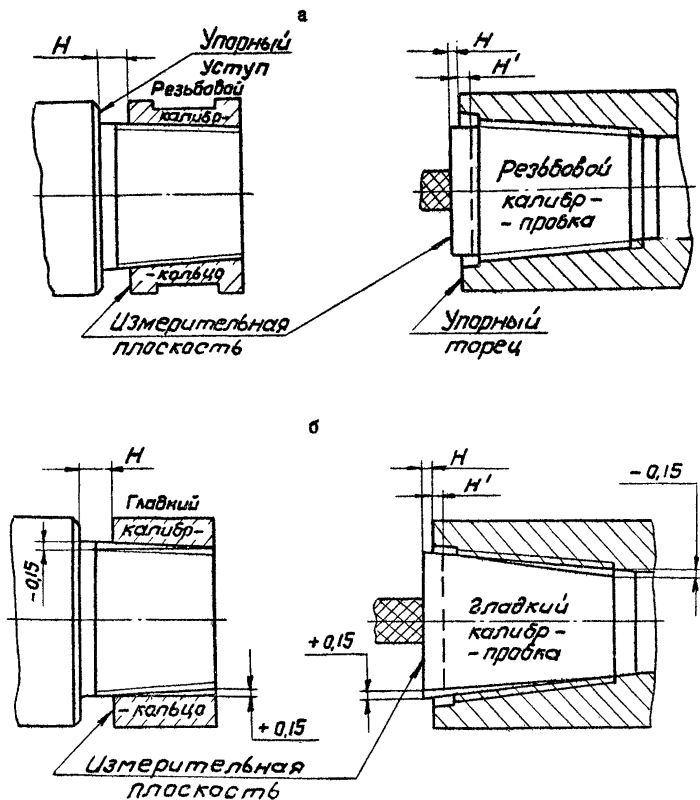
Проверка калибрами резьбового соединения с наружным упором.
